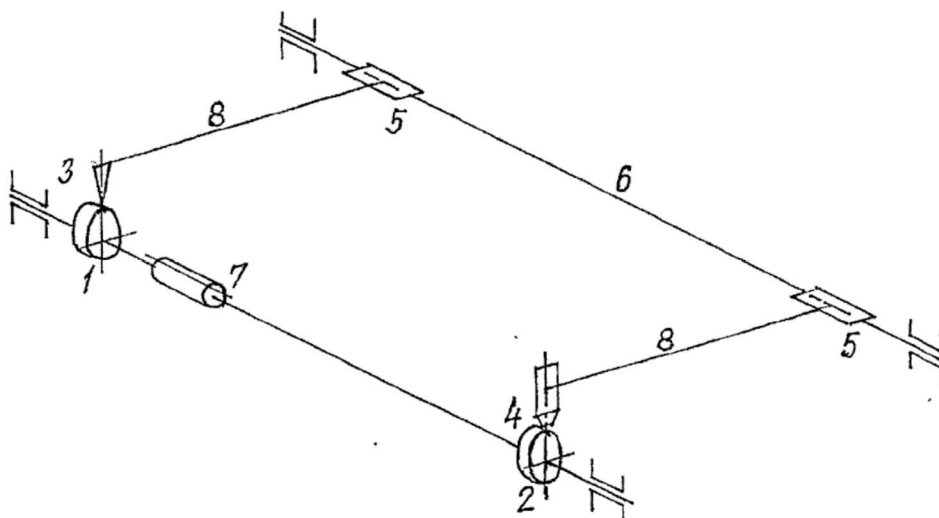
Схема копіювального обладнання наплавочної установки 1
